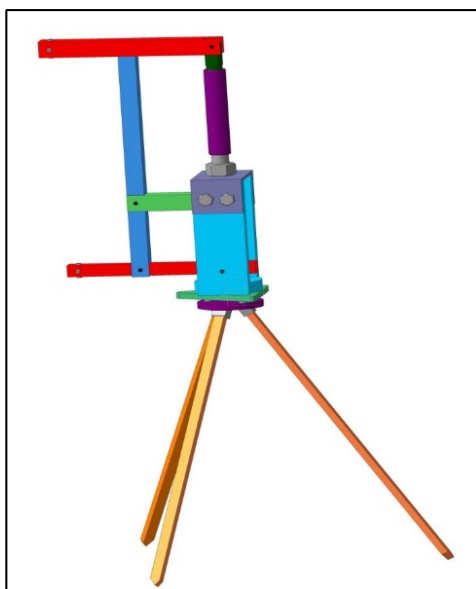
Опытный образец, макет двухлучевого лазерного визира
